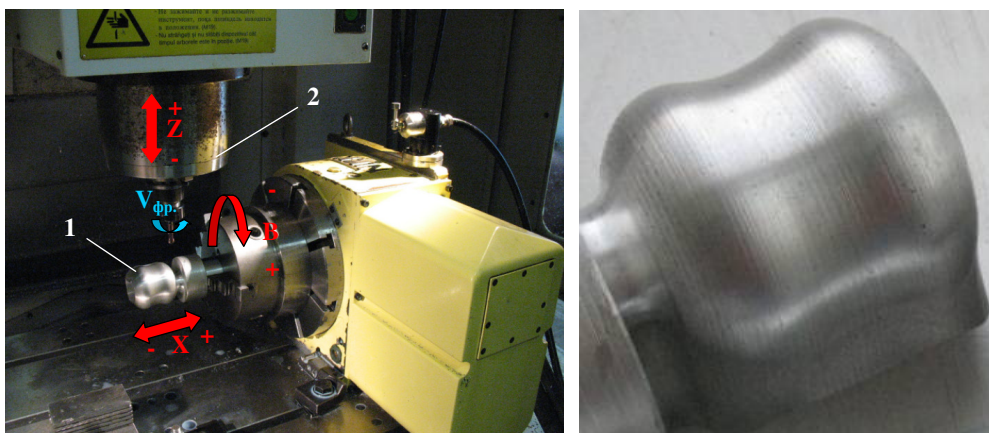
Схема формоутворення та оброблений експериментальний зразок
